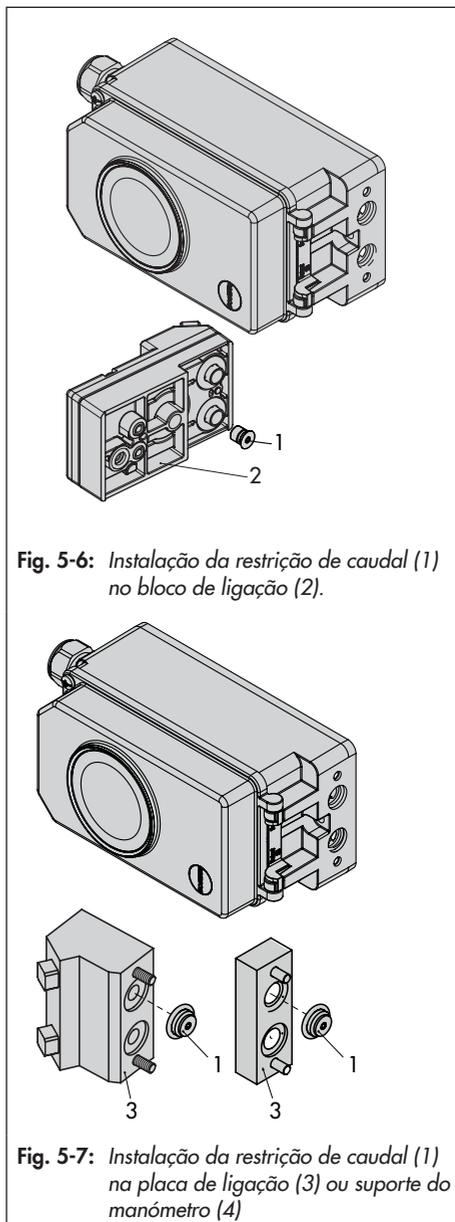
Instalação da restrição de caudal (1) no bloco de ligação (2).
